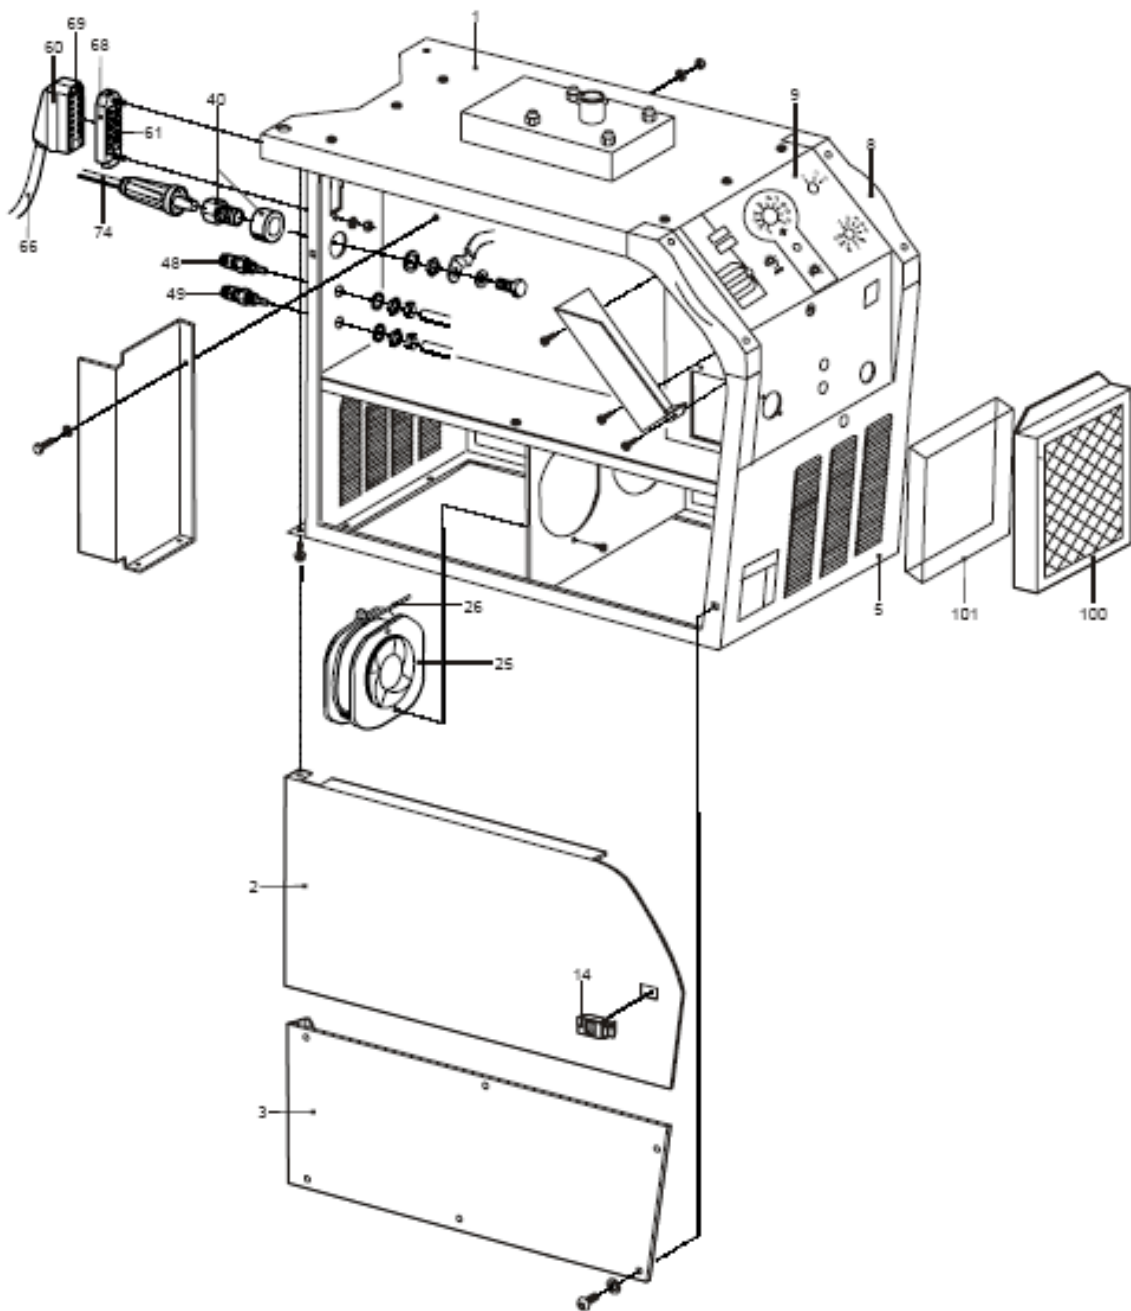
explosietekening Epsilon 300-4S ÷ 450-4WS (rechts)
